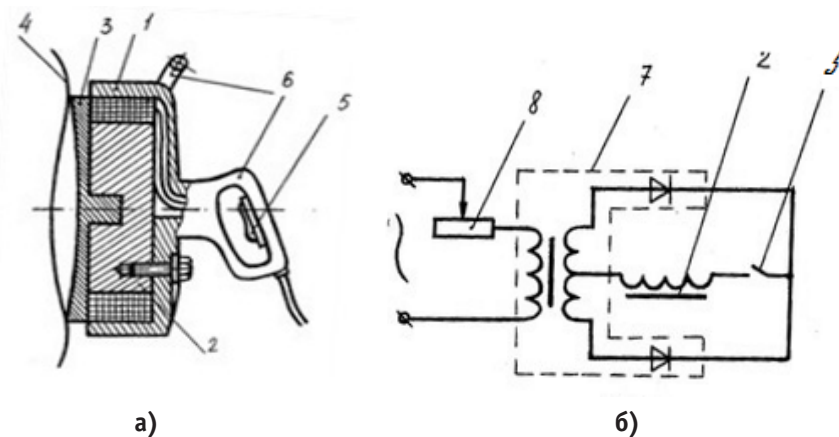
Электромагнитное устройство для правки кузовов автомобилей: а — схема устройства, б — электрическая схема: 1. Корпус; 2. Электромагнит; 3. Оправка; 4. Деформированная поверхность детали; 5. Выключатель; 6. Рукоятка. 7. Выпрямитель; 8. Реостат.
